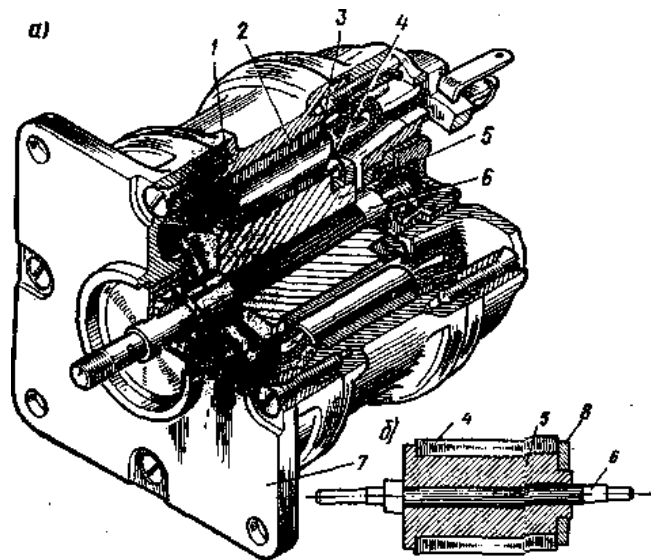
Устройство гистерезисного двигателя: 1— корпус; 2 — пакет статора; 3 — обмотка статора; 4 — кольцо из магнитно-твердого материала; 5 — ротор; 6 — вал; 7 — фланец; 8— запорное кольцо
